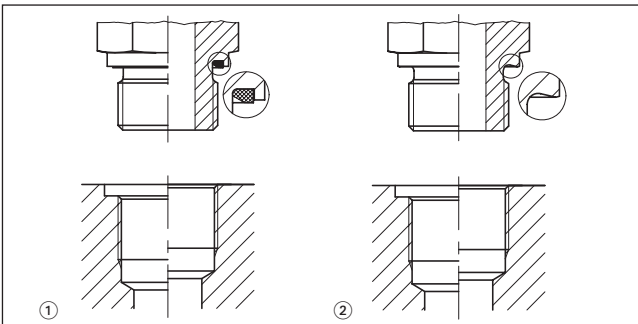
① O-Ring mit Stützring; ② Form A
